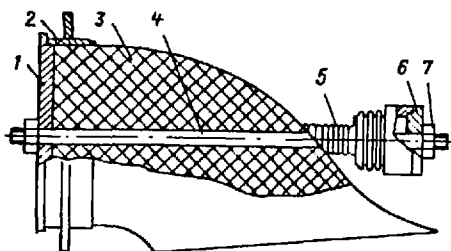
Схема приспособления для установки корпуса дейдвудного подшипника. 1 — диск, центрирующий гребной вал в статоре; 2 — статор; 3 — болван водозаборника; 4 — фальшвал; 5 — корпус дейдвудного подшипника; 6 — диск, центрирующий вал в корпусе 5; 7 — гайка М20.
